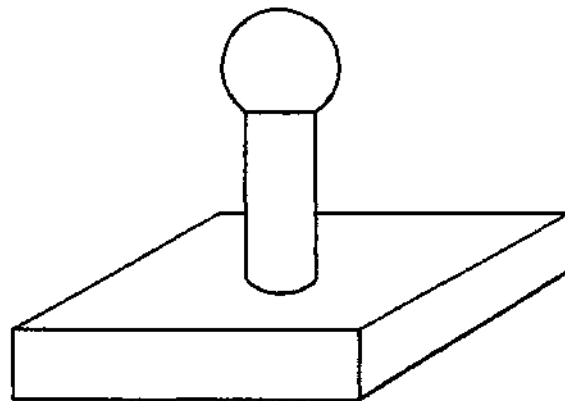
Відривний металевий елемент квадратної форми
